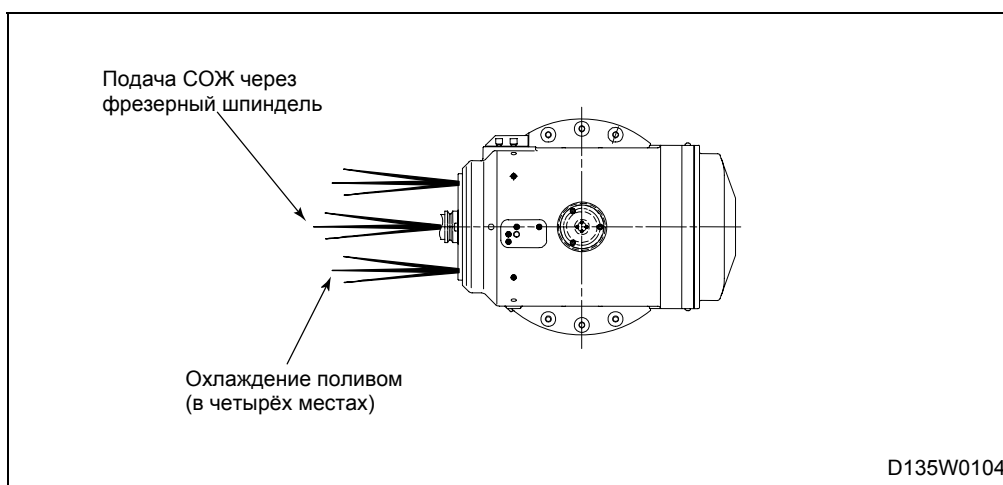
Подача СОЖ поливом и подача СОЖ через фрезерный шпindel
